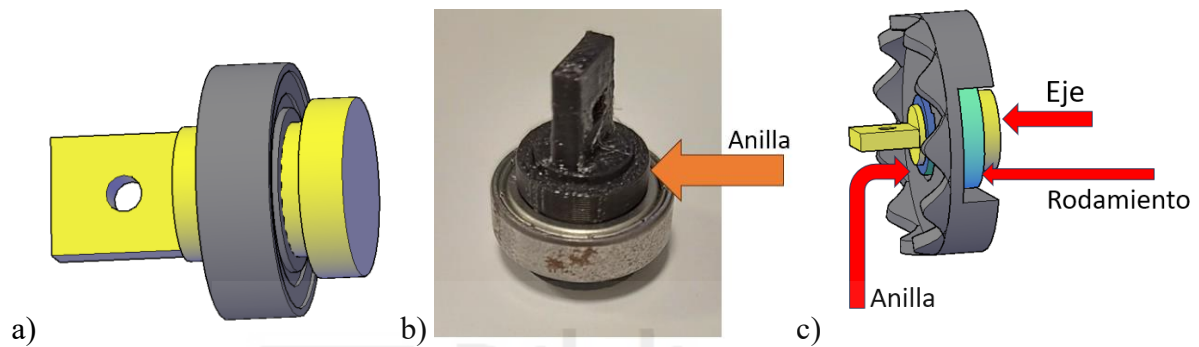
a) Inserción del eje del tambor en el rodamiento, b) Inserción del eje del tambor en el rodamiento junto a la anilla de retención, c) Montaje final de los elementos anteriores en el tambor.
